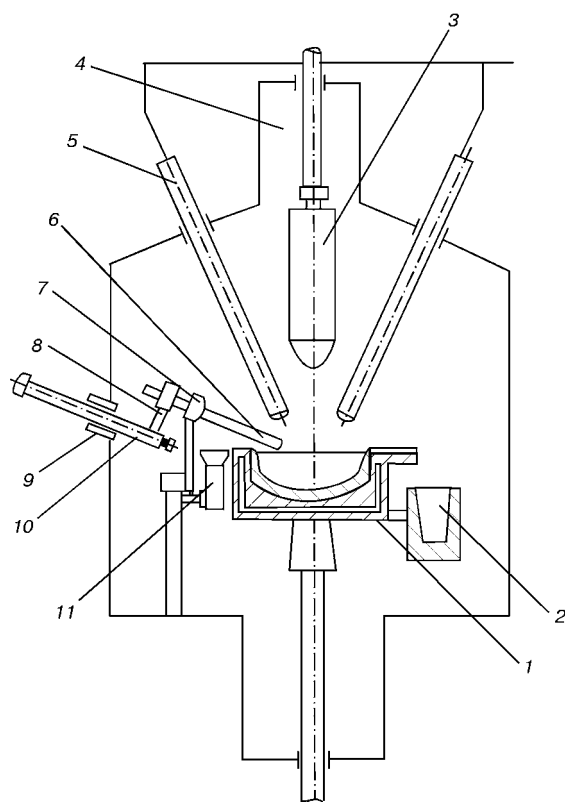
Схема модернизированной 4-плазмотронной лабораторной установки УПП-3: 1 — гарнисажный тигель; 2 — изложница; 3 — прессованная заготовка; 4 — камера; 5 — плазмотрон; 6 — водоохлаждаемый наконечник; 7 — отсекагель; 8 — держатель; 9 — уплотнение; 10 — шток; 11 — накопитель
